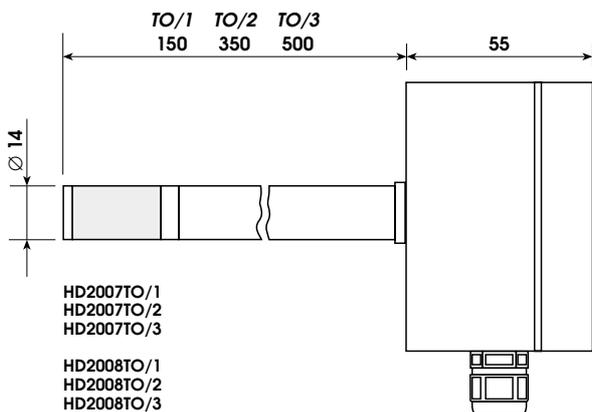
Dimensioni meccaniche versione TO - TO version: mechanical dimensions - Dimensions mécaniques version TO - Version TO, Abmessungen - Dimensiones mecánicas versión TO
